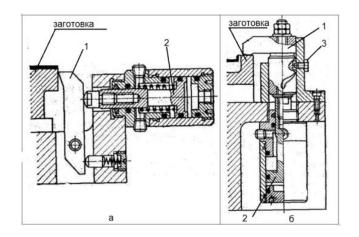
Примеры использования встроенных цилиндров: а – ось цилиндра расположена горизонтально; б – ось цилиндра расположена вертикально
